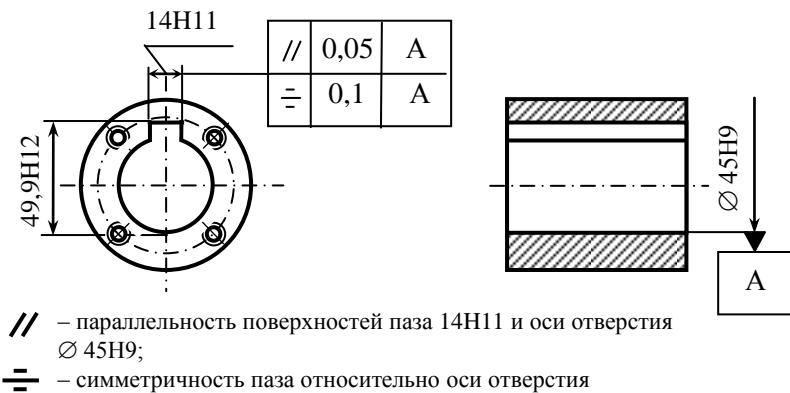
Пример назначения размеров и допусков на шпоночный паз в отверстии ступицы (на рабочем чертеже детали) с указанием допусков на расположение паза относительно базового отверстия А
